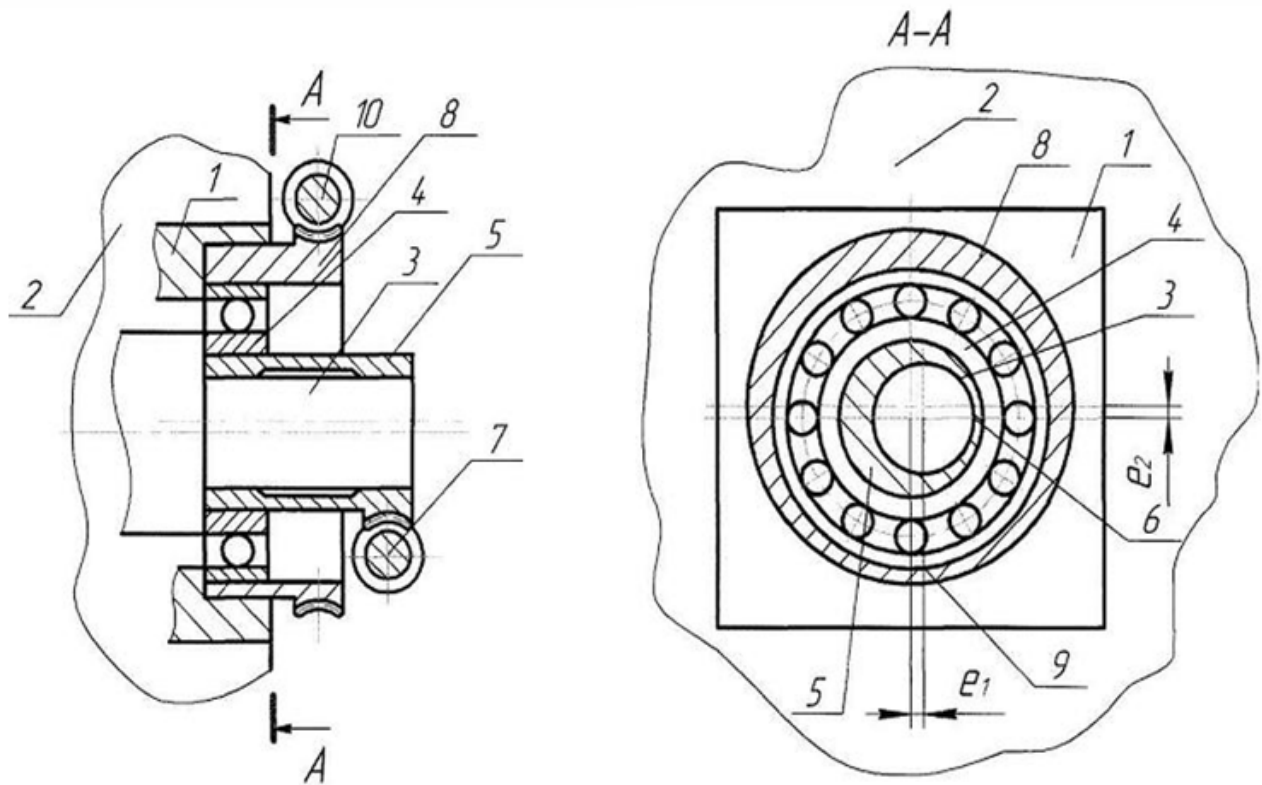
Механізм регулювання перехрещення валків: 1 – Корпус підшипника; 2 – Станина; 3 – Цапфа валка; 4 – Підшипник; 5 – Внутрішня ексцентрична втулка; 6 – Отвір внутрішньої втулки; 7 – Механізм повороту внутрішньої втулки; 8 – Зовнішня ексцентрична втулка; 9 – Ексцентричний отвір зовнішньої втулки; 10 – Механізм повороту зовнішньої втулки
